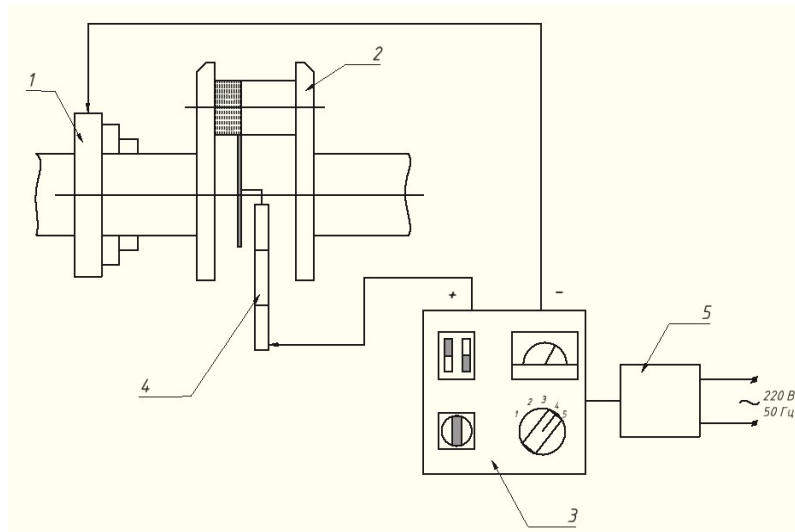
Принципова схема роботи експериментальної установки зміцнення деталей: 1 – токарний верстат типу ДІП – 500; 2 – колінчастий вал; 3 – силовий блок та блок управління установки ДЗ; 4 – електродний утримувач; 5 – фільтр мережі
